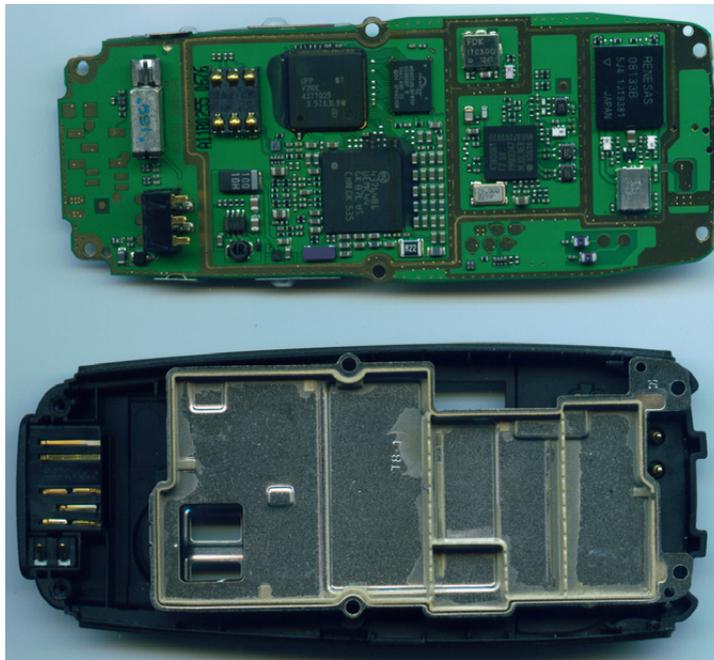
Alle elektrischen Komponenten des Handys befinden sich auf der Platine.
